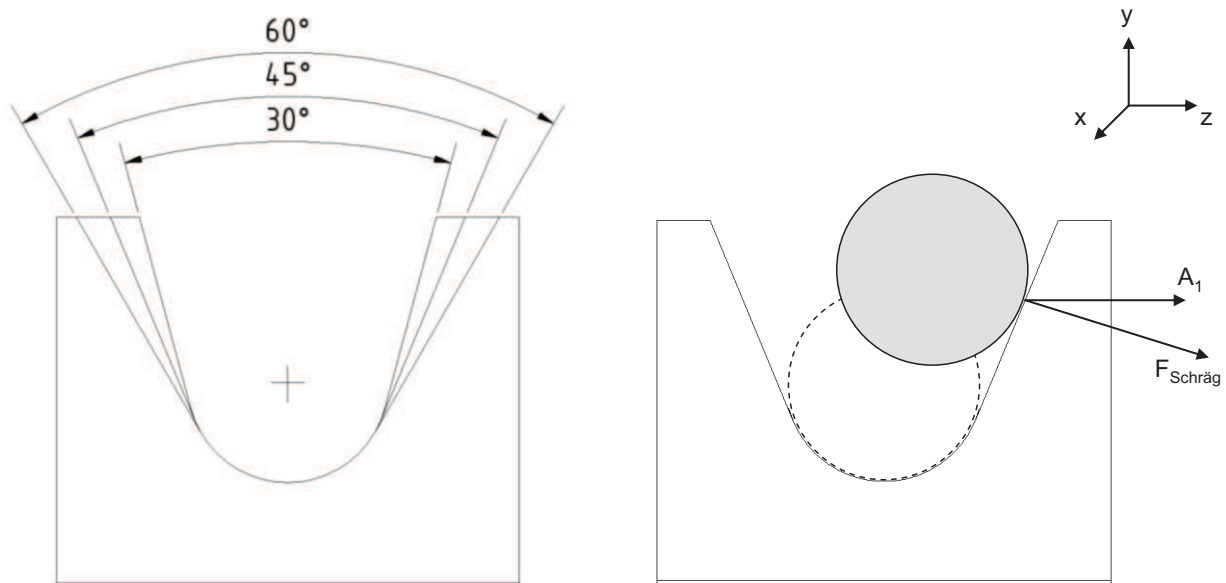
(links) Rillenöffnungswinkel; (rechts) Kräfte auf Rillenflanke bei Schrägzug
